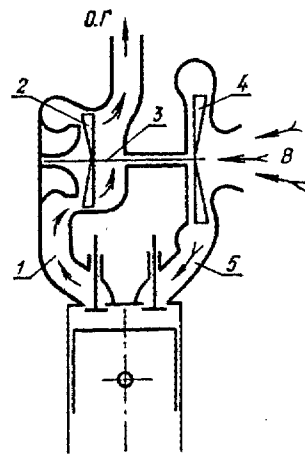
Схема действия турбокомпрессора: 1 – выпускной канал; 2 – колесо турбины; 3 – вал; 4 – колесо компрессора; 5 – воздушный канал
